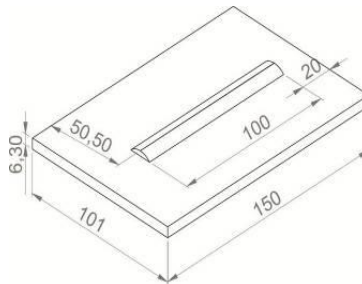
Dimensões, em milímetros, dos corpos de provas utilizados e dos cordões de solda
